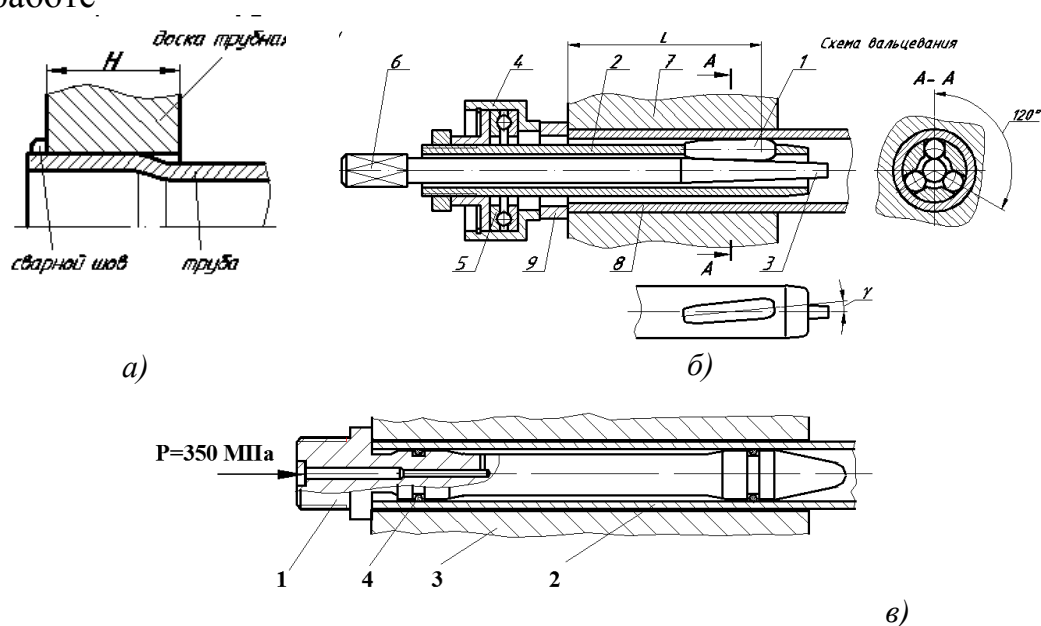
Общий вид узла крепления теплообменной трубы и методы закрепления: а – узел крепления; б - роликовое вальцевание: 1- ролики; 2- корпус; 3- веретено; 4- обойма; 5- подшипник; 6- хвостовик; 7-доска трубная; 8- труба; в- гидрораздача: 1- зонд; 2- труба; 3- доска трубная; 4- уплотнительные кольца)
